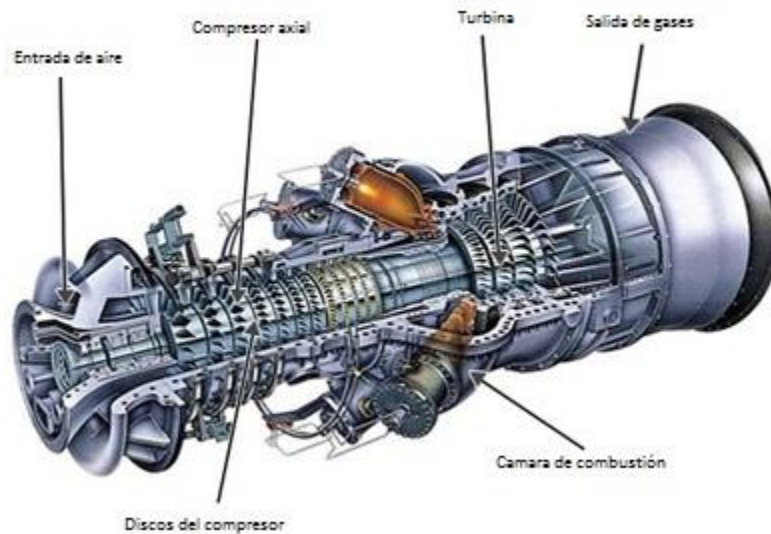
Componentes principales de una turbina de gas (modificado de UNICORP, s.f.).
